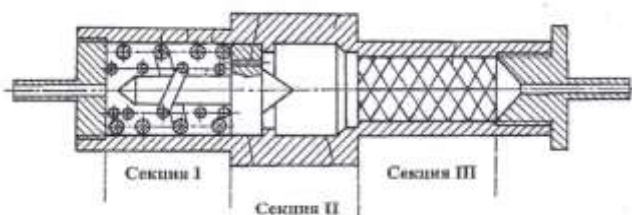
Комбинированный смеситель-механоактиватор прямооточного типа
